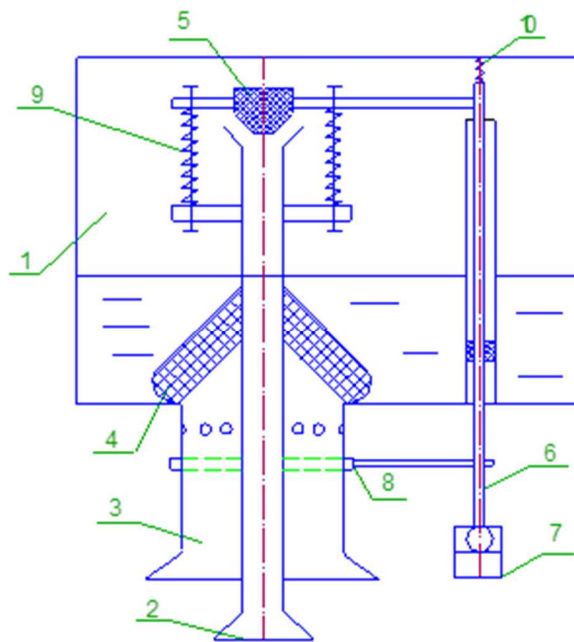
Схема дозувального пристрою з керуванням копиром: 1 – резервуар; 2 – газова трубка; 3 – зливна трубка; 4 – рідинний клапан; 5 – газований клапан; 6 – шток; 7 – копир; 8 – повітряний клапан; 9, 10 – пружини
